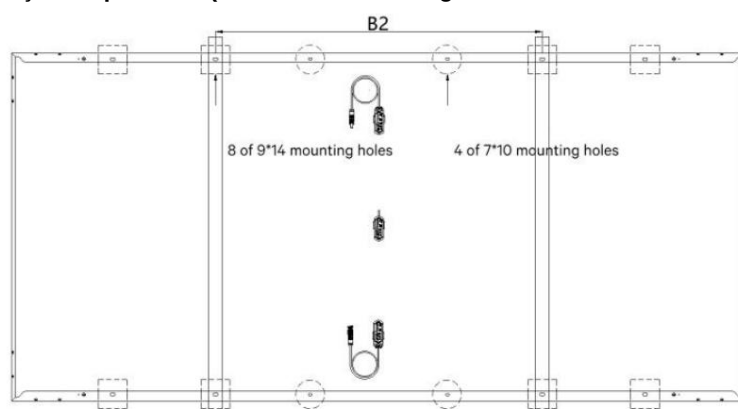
Método de fixação por parafuso (8 orifícios de montagem - instalação interna de 4)
